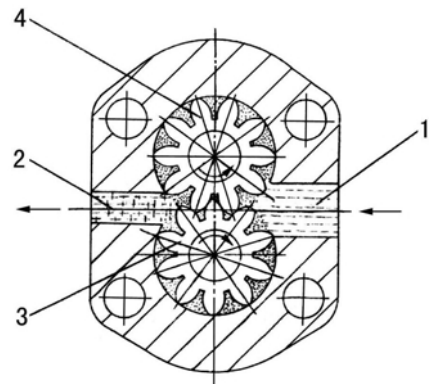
Principio de funcionamiento de la bomba de engranajes
